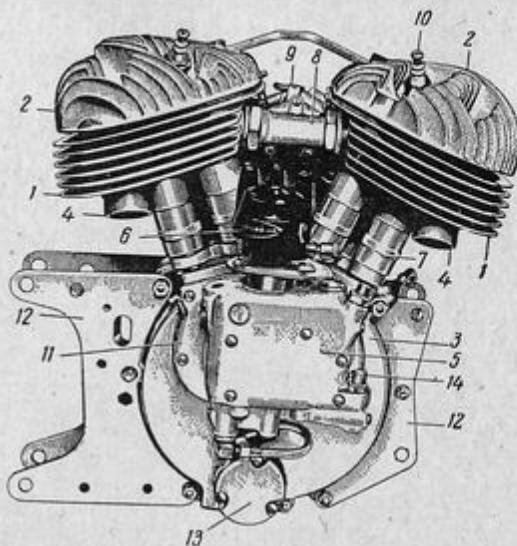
Четырехтактный двухцилиндровый двигатель Индиан 741-В с рабочим объемом 500 см³:
